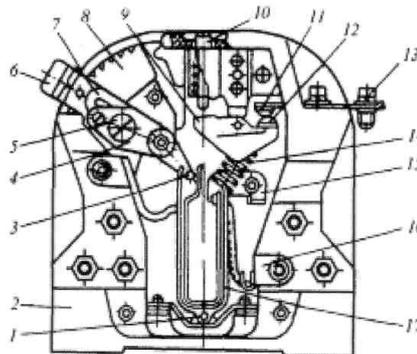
Тепловое реле ТРТ: 1- ось биметаллической пластины; 2 - изоляционный корпус; 3 - ролик рычага; 4 - поводок; 5 - эксцентрик; 6 - ручка рычага; 7 - пластинчатая пружина; 8 - сектор уставки; 9 - колодка; 10 - кнопка для принудительного восстановления реле; 11 - неподвижный блокировочный контакт; 12 - подвижный мостиковый контакт; 13 - выводы блокировочных контактов; 14 - пружина; 15 - упор; 16 - вывод биметаллической пластины; 17 - биметаллическая пластина.
